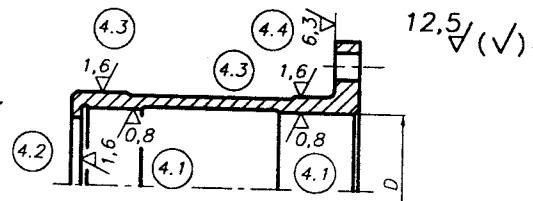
Рекомендуемая шероховатость поверхностей
